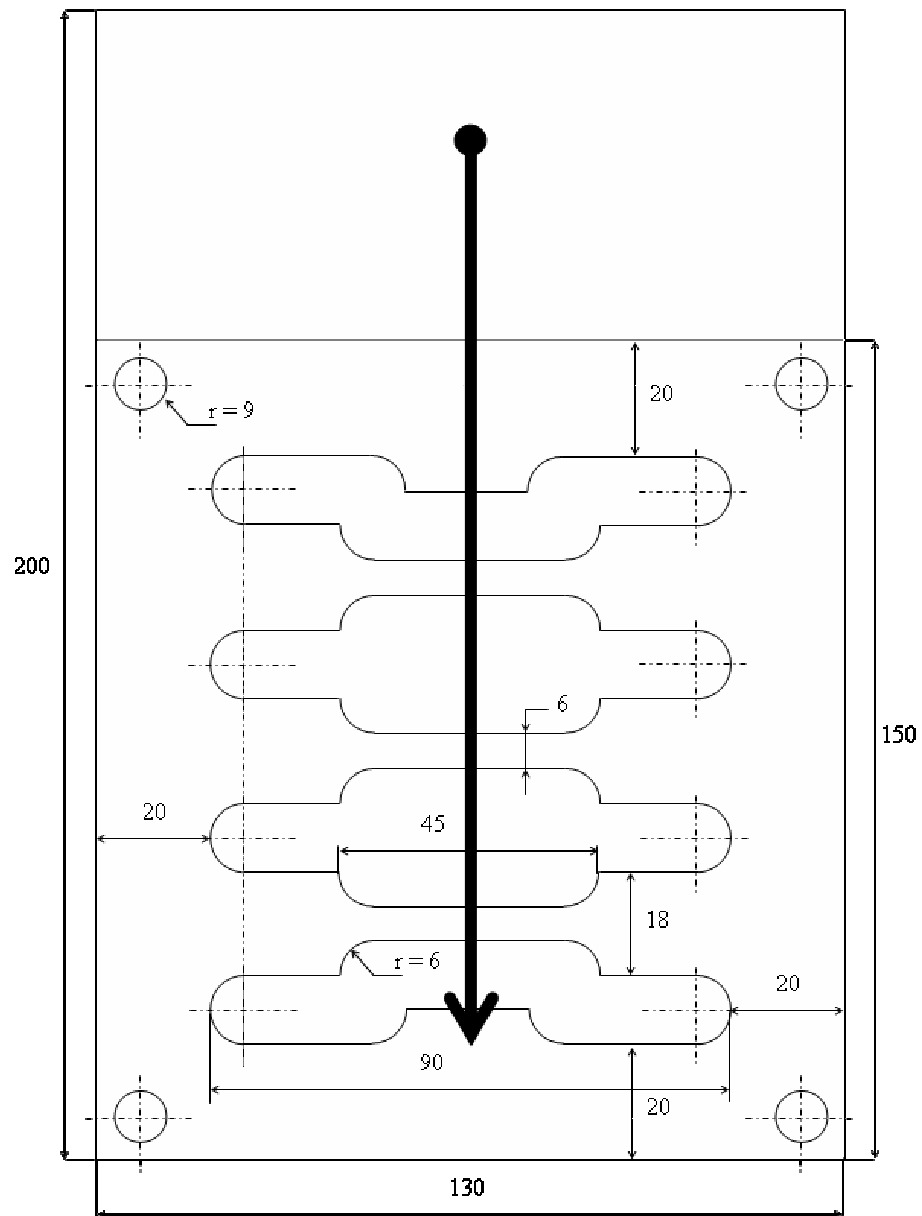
Plan d'usinage des éprouvettes de traction
